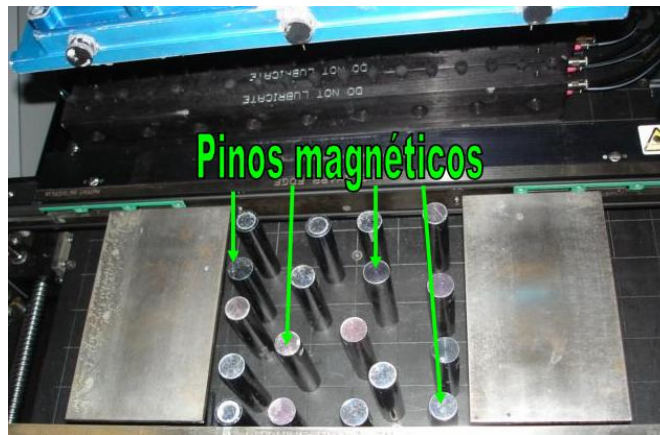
Ferramenta de suporte do PCB tipo “pinos magnéticos”
